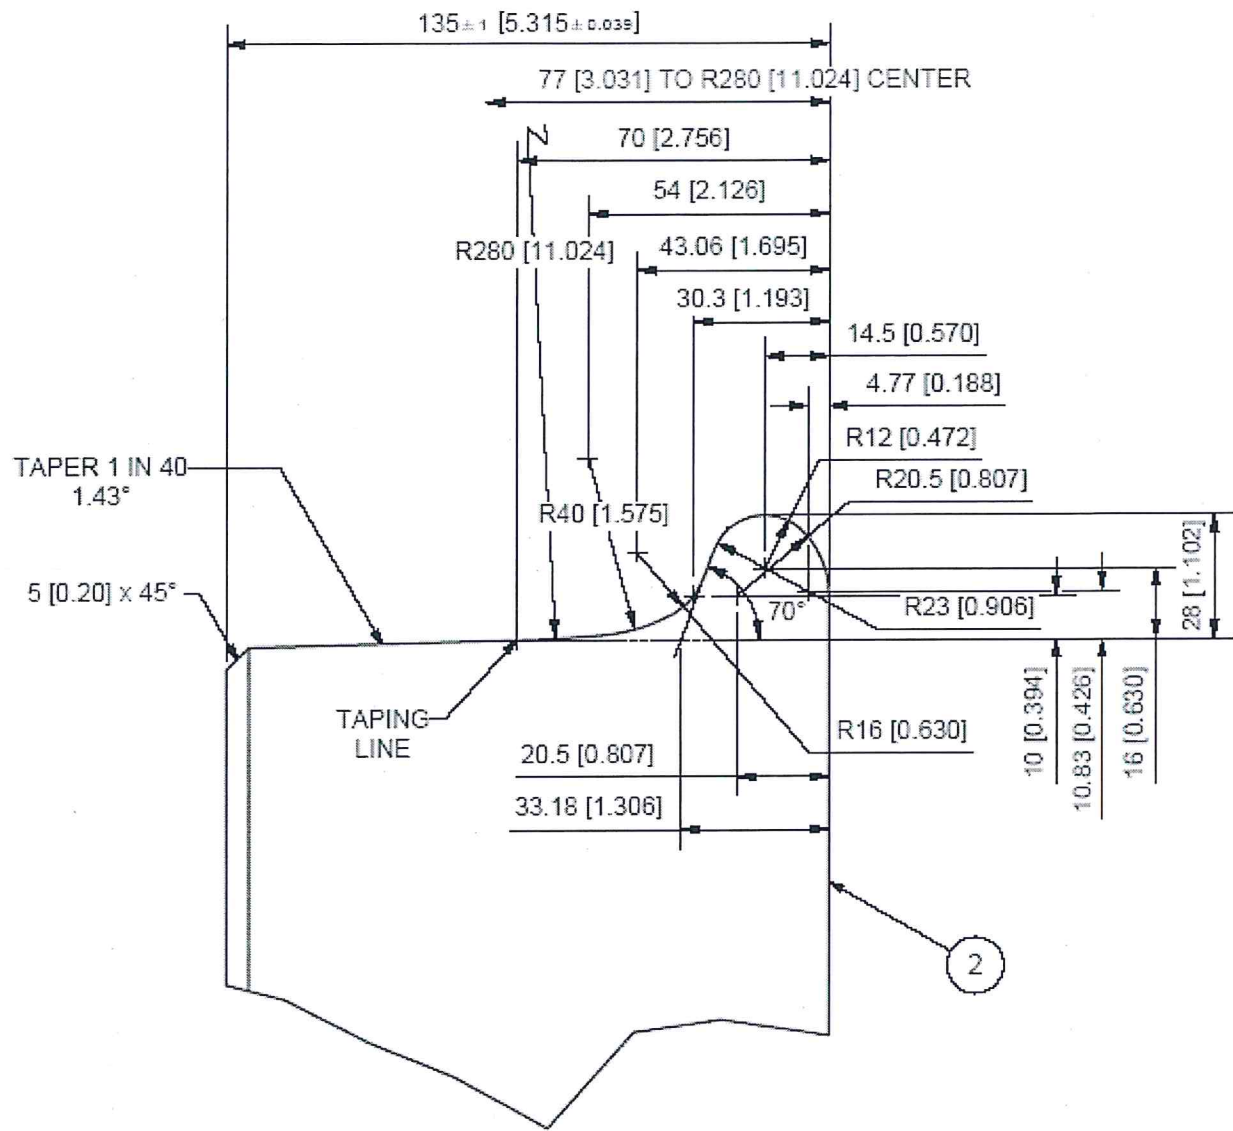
Perfil de rodadura del aro de rueda (dimensiones en milímetros)
